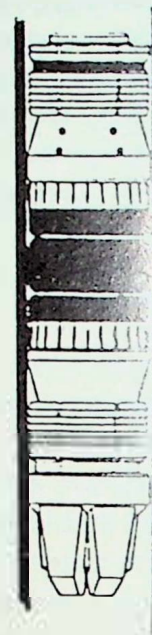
Pose d'un bouchon à l'aide d'un joint en caoutchouc
